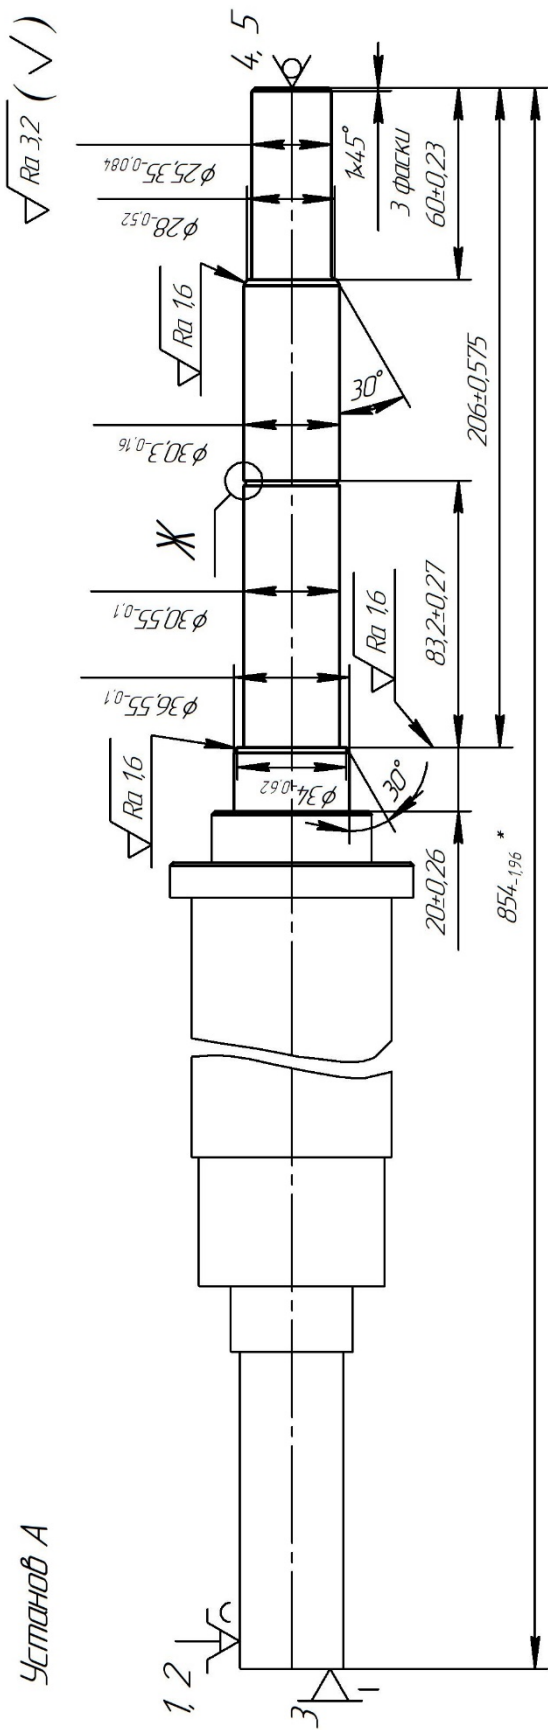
Альтернативна схема базування заготовки на операції токарній з ЧПК 025, установ А
